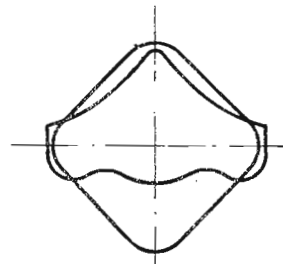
Способ задачи в угловой калибр, когда размеры заготовки недостаточны
